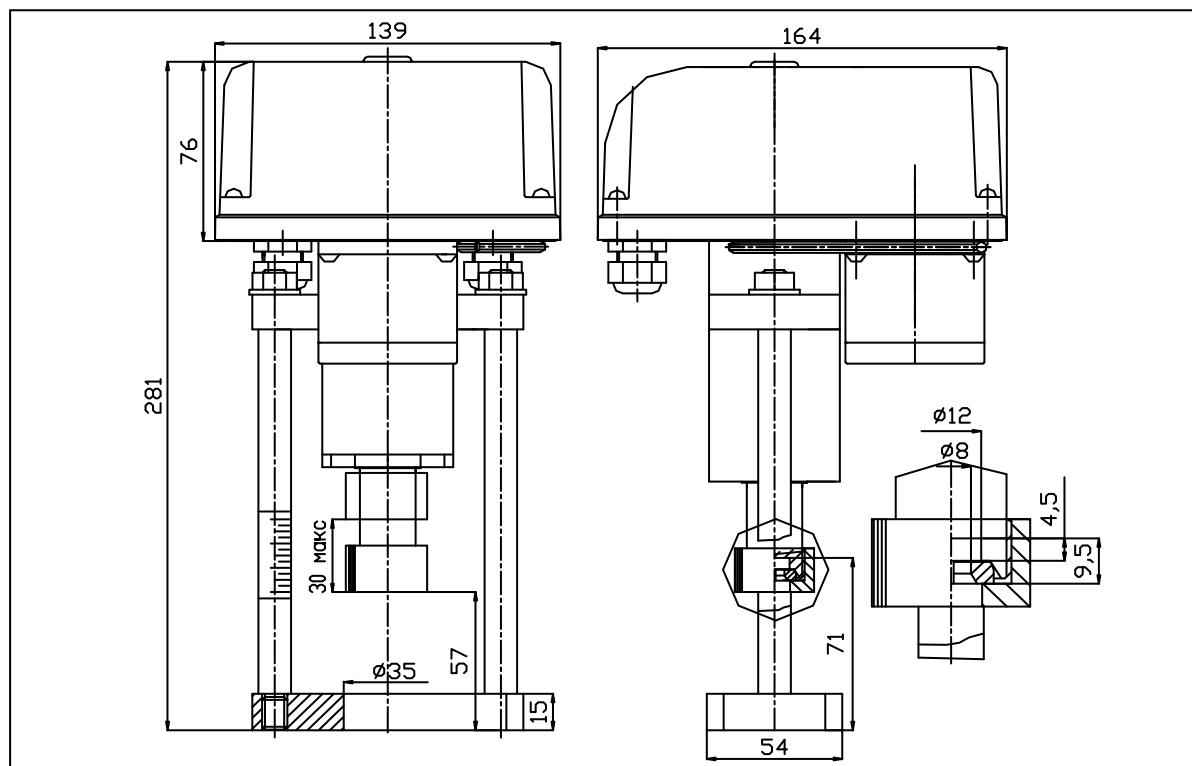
Габаритные, установочные и присоединительные размеры механизма
